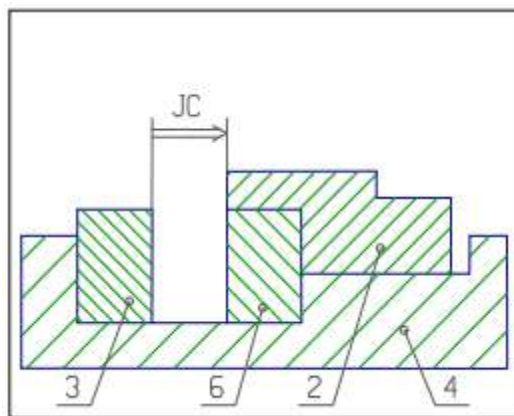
Exemple : Deux pièces à l'origine ou à l'extrémité du jeu
